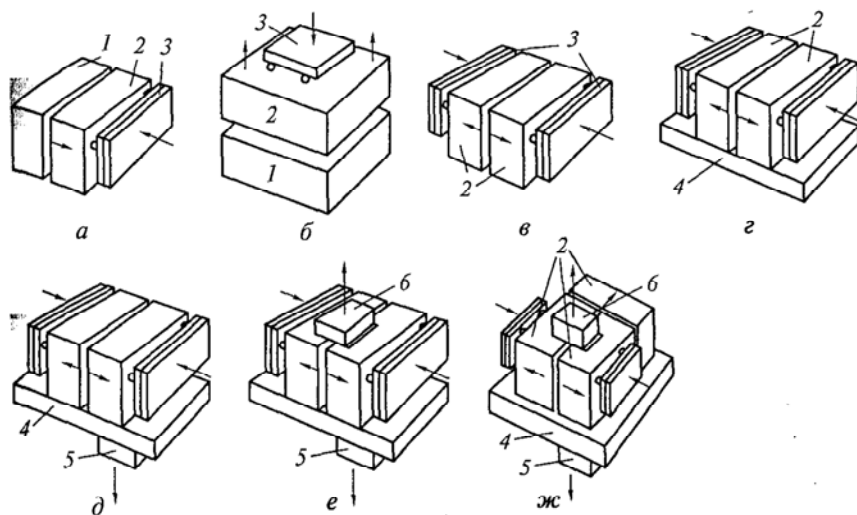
Типы кокилей для универсальных кокильных машин (стрелки – направление движения деталей кокиля):
